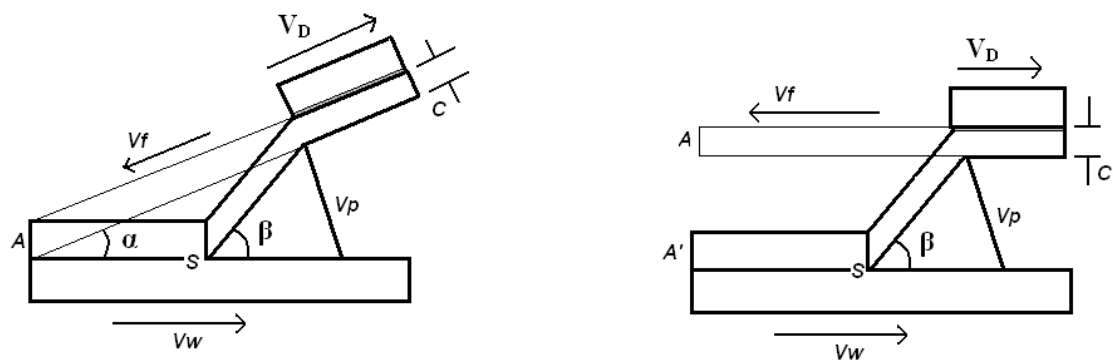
Variables presentes en los arreglos de la Soldadura por Explosión
